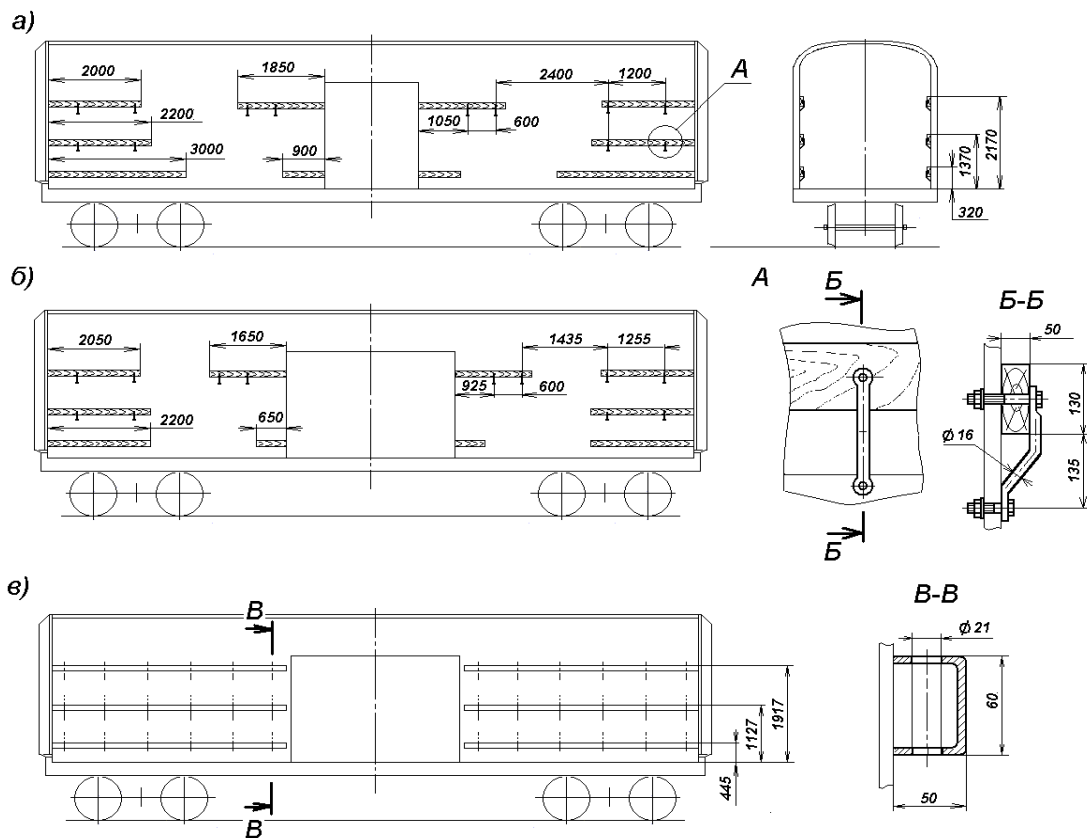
Примеры размещения крепежных устройств на балках в вагонах с несъемным оборудованием:
